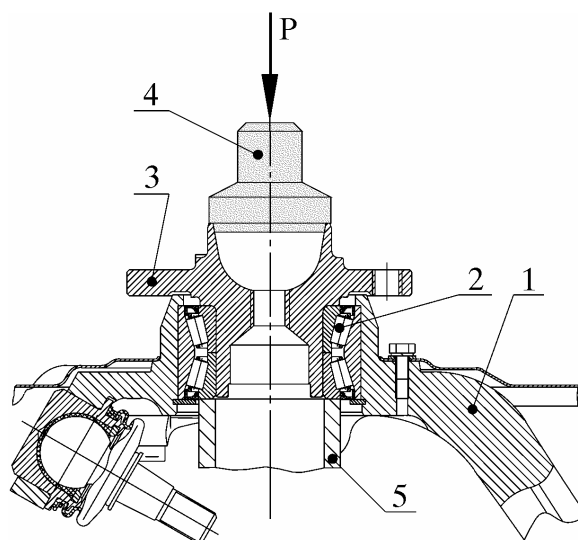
Запрессовка ступицы колеса во внутреннее кольцо подшипника: 1 - поворотная стойка; 2 - подшипник; 3 - ступица, дет. 3111-3103015; 4 - оправка; 5 - приспособление
